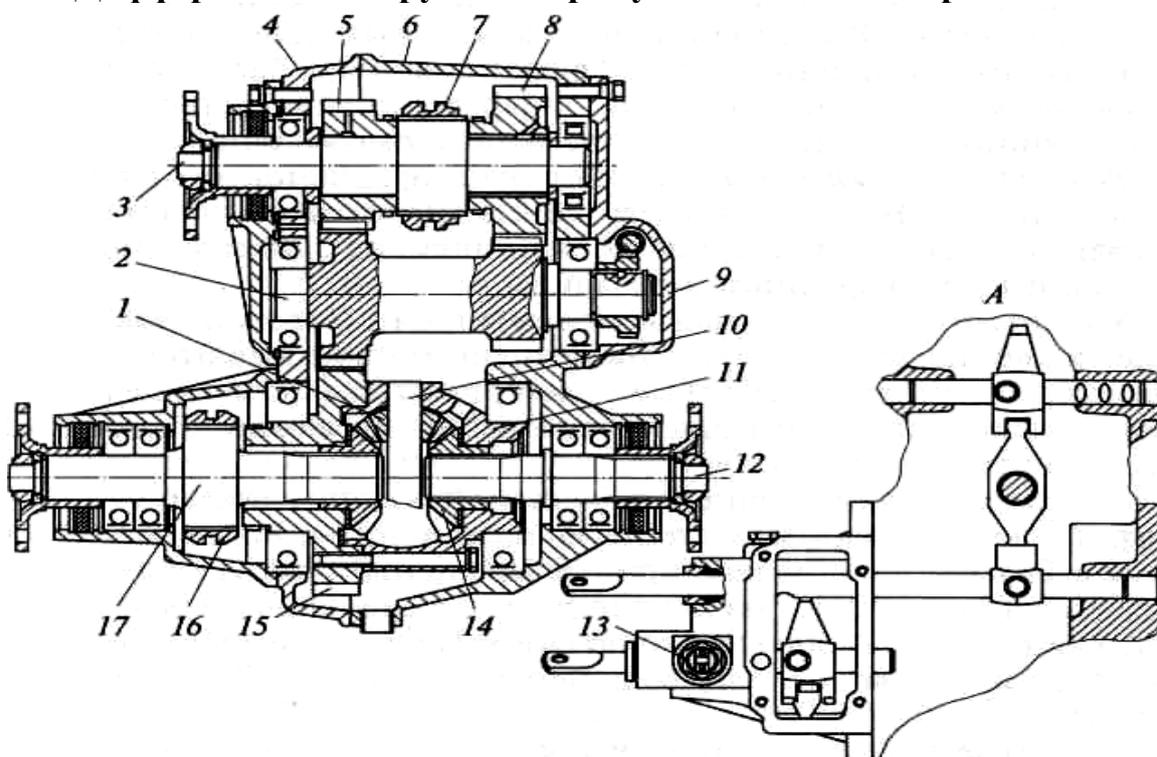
Раздаточная коробка полноприводных автомобилей «ГАЗель»: 1 — сателлит; 2 — промежуточный вал; 3 — ведущий вал; 4 — передний картер; 5 — шестерня понижающей передачи; 6 — задний картер; 7 — муфта переключения передач; 8 — шестерня высшей передачи; 9 — крышка; 10 — ось сателлита; 11 — корпус дифференциала; 12 — вал привода заднего моста; 13 — датчик; 14 — молуосевая шестерня; 15 — шестерня дифференциала; 16 — муфта блокировки дифференциала; 17 — вал привода переднего моста; А — механизм управления раздаточной коробкой.
